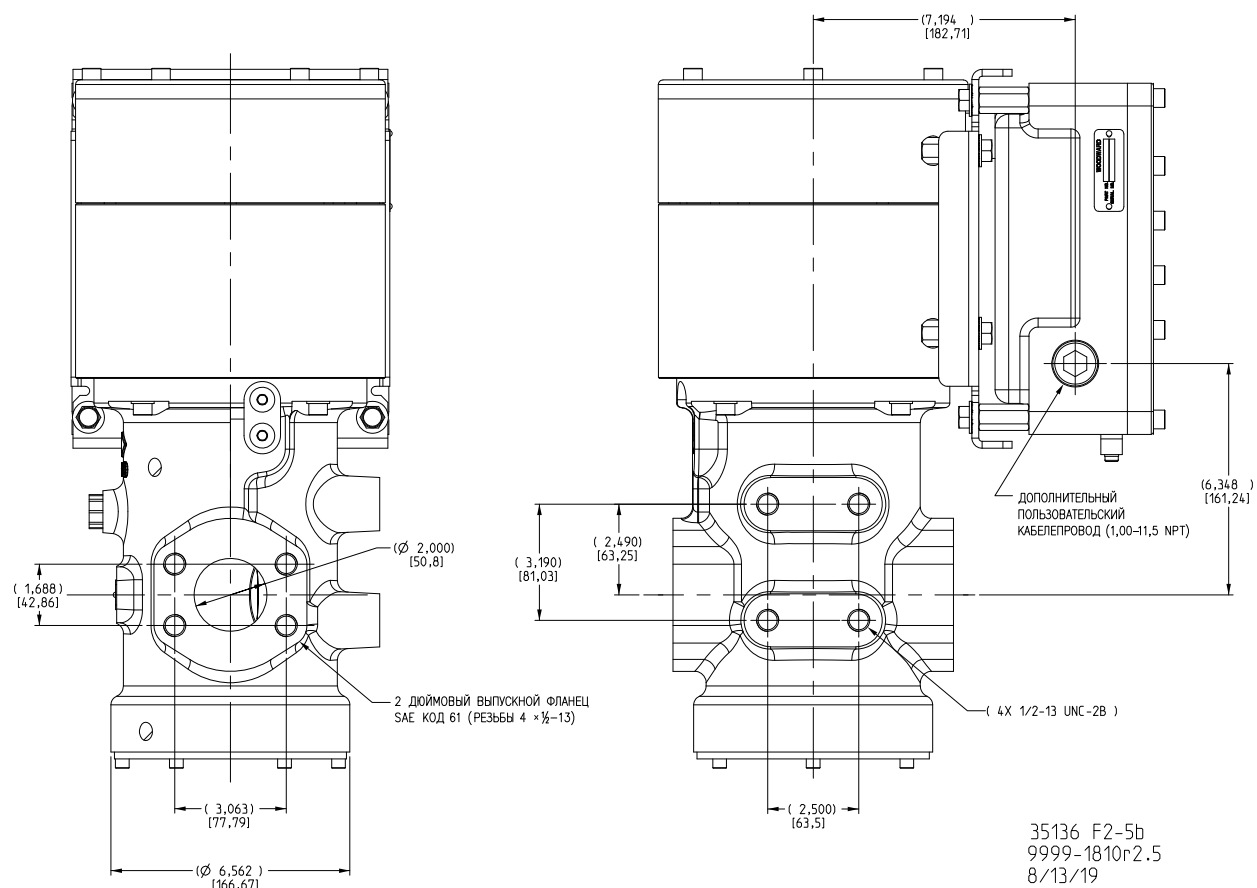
Габаритно-присоединительный чертеж, алюминий, GS50 с кабельными вводами
